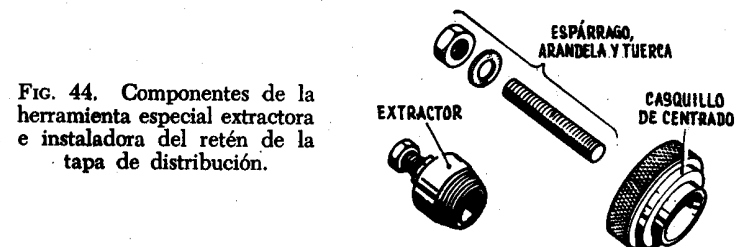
Componentes de la herramienta especial extractora e instaladora del retén de la tapa de distribución.
